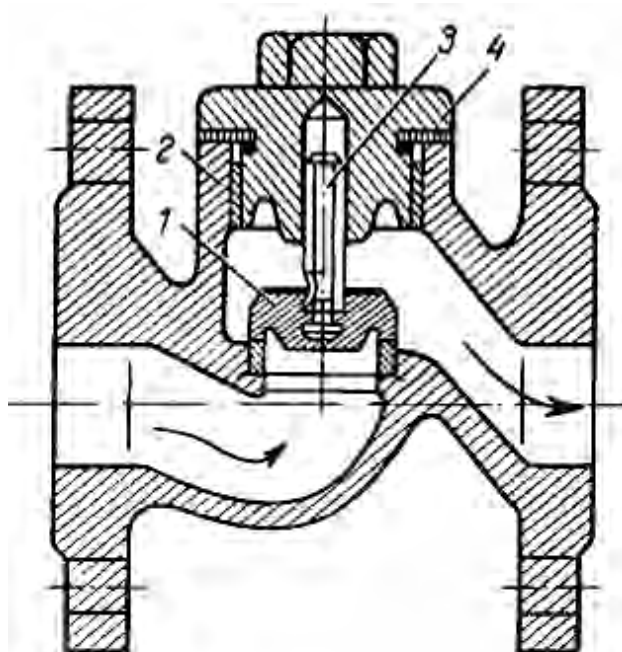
Устройство подъемного обратного клапана: 1 – седло клапана; 2 – корпус; 3 – шток клапана; 4 – крышка с каналом для штока
